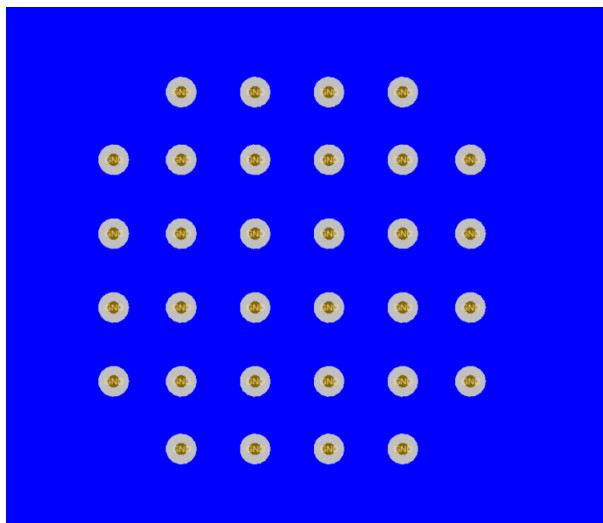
LMK5C33414A 的 PCB 布局示例，底层
